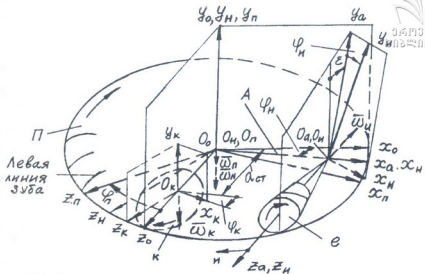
Станочное зацепление при нарезании некруглых торцевых зубчатых колес с левыми линиями зубьев
